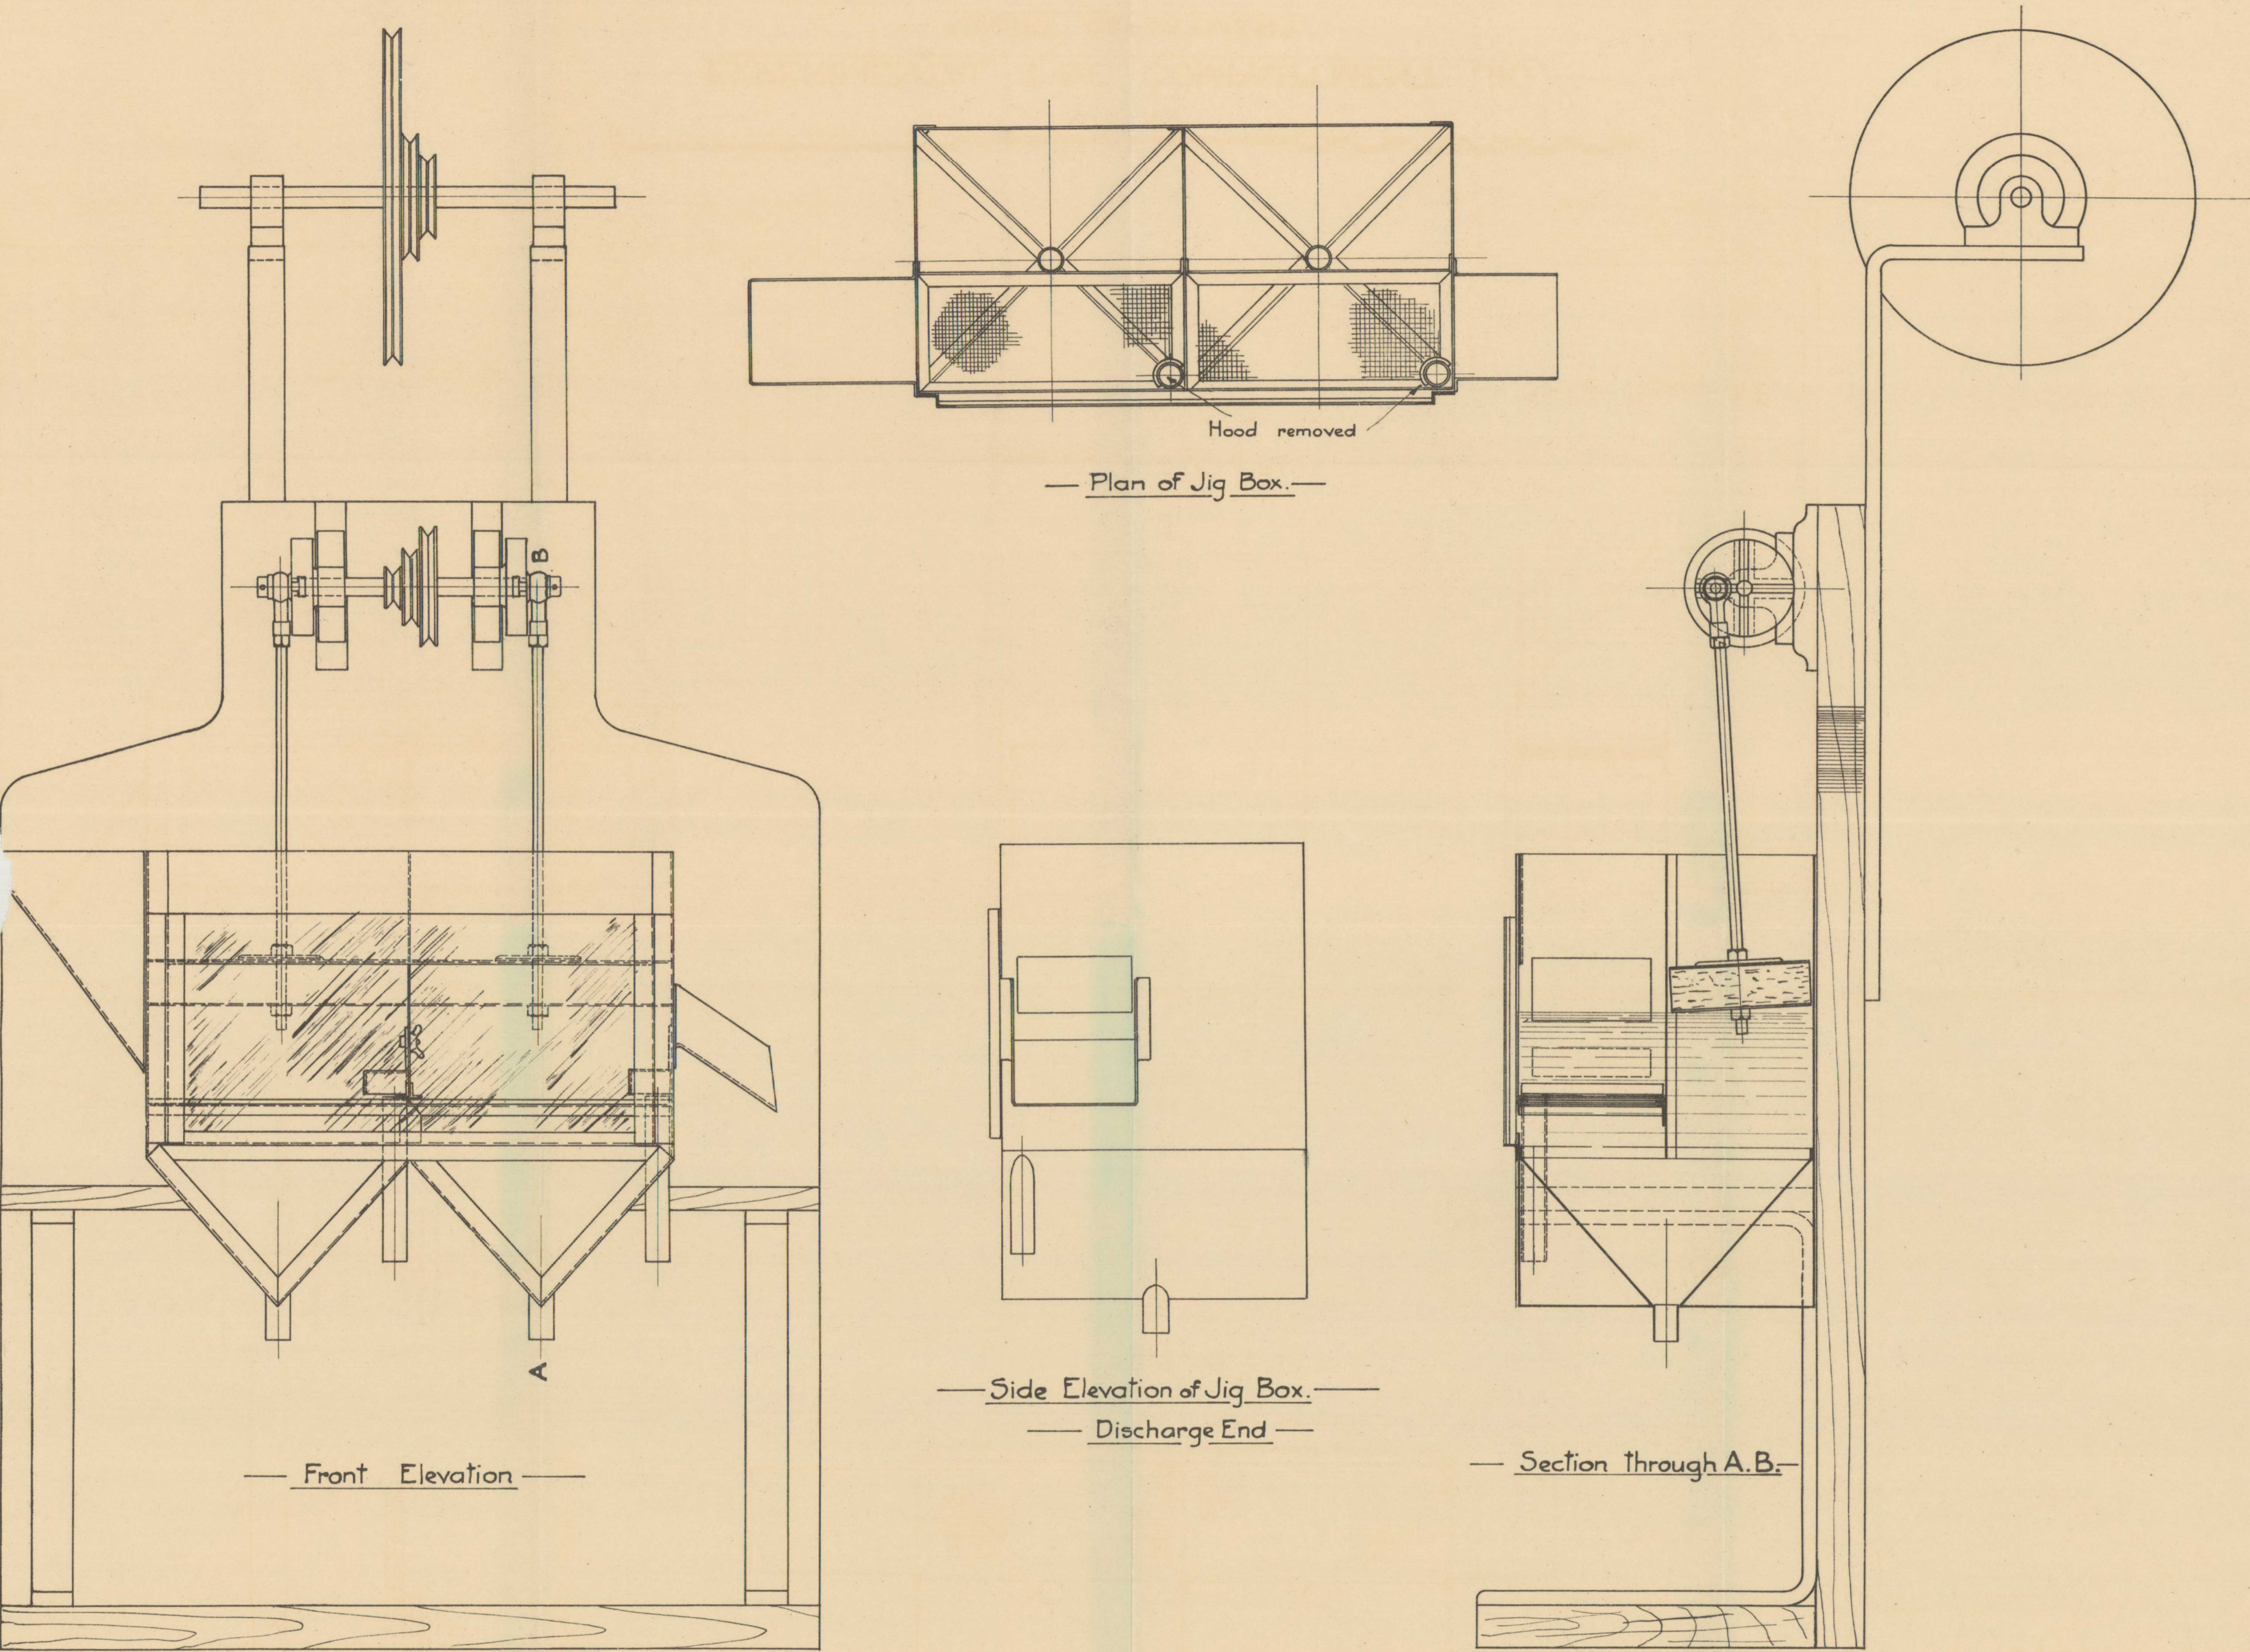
Élévation coupe d'une installation de laveurs Jeffrey-Robinson.
